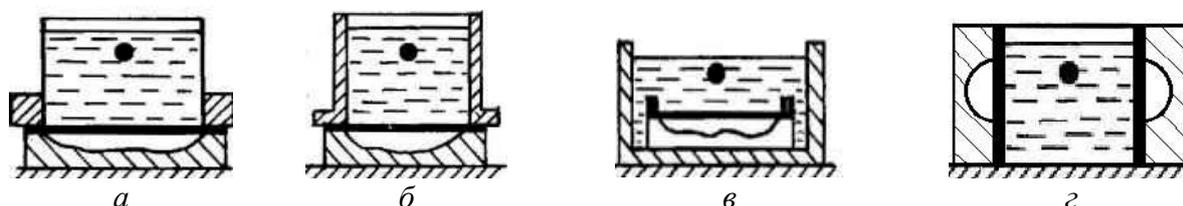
Типовые схемы взрывной штамповки из листовых заготовок:
